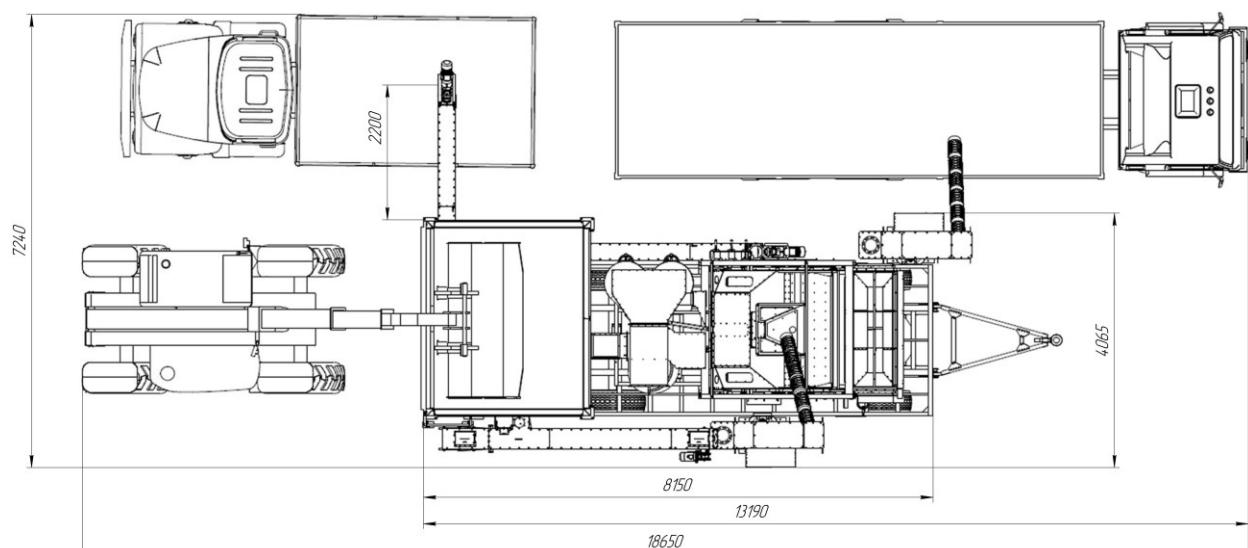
Габаритный чертеж мобильного зерно-семяочистительного агрегата для внутрихозяйственного использования в рабочем положении
